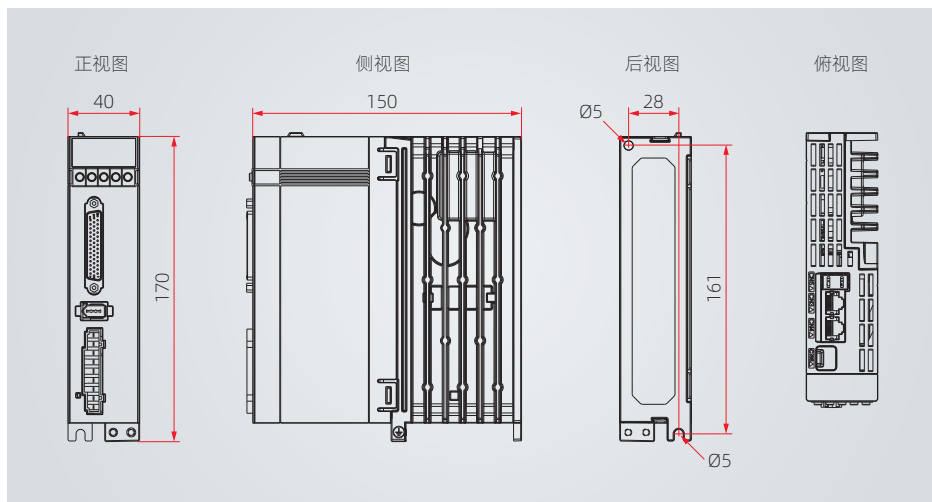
驱动器 (SIZE A) 安装尺寸示意图 (单位: mm)
